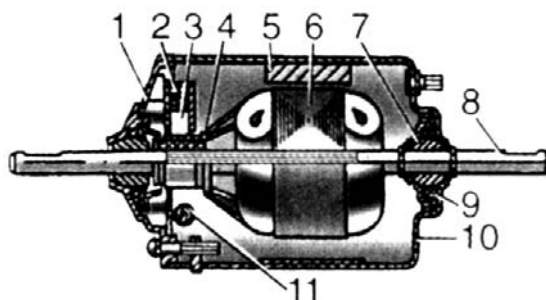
Электродвигатель 511.3730: 1 – крышка; 2 – пружина; 3 – щетка; 4 – коллектор; 5 – магнит; 6 – якорь; 7 – подшипник; 8 – вал; 9 – фетровая шайба с запасом смазки; 10 – корпус; 11 – фильтр радиопомех
